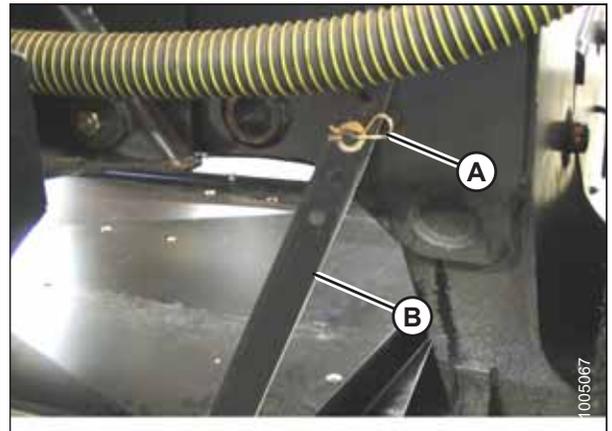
Ремень формовочного щитка на опоре колеса
